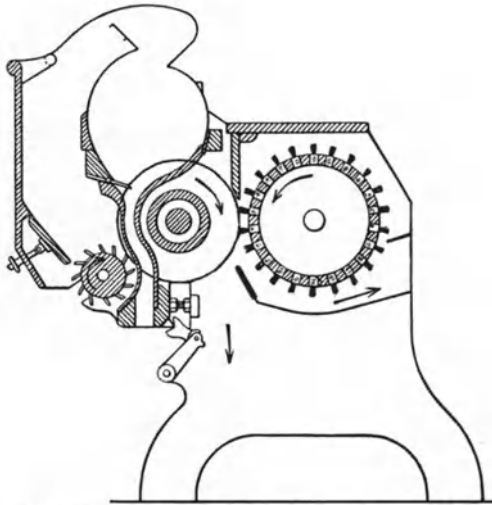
Säge-Egreniermaschine mit Bürstenabführung für das entkörnte Fasergut.
